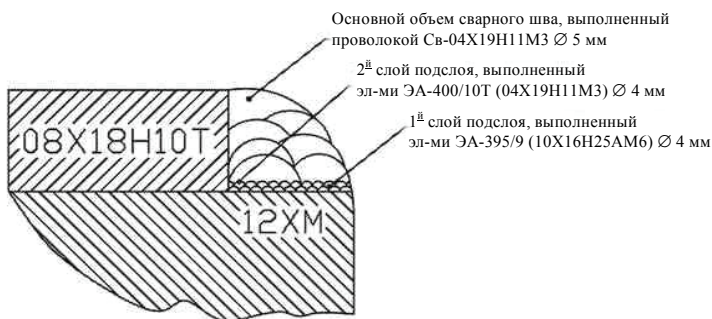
Схема комбинированной сварки пакета: РДС (переходной подслоя), АДС (основной объем сварного шва пакета)
